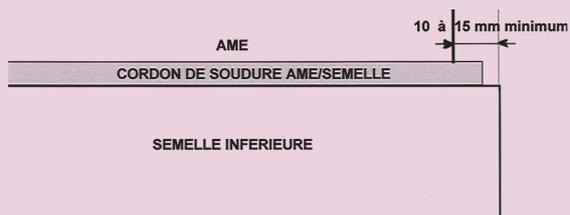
Contournement des semelles nécessaire au retournement des soudures âme-semelles
